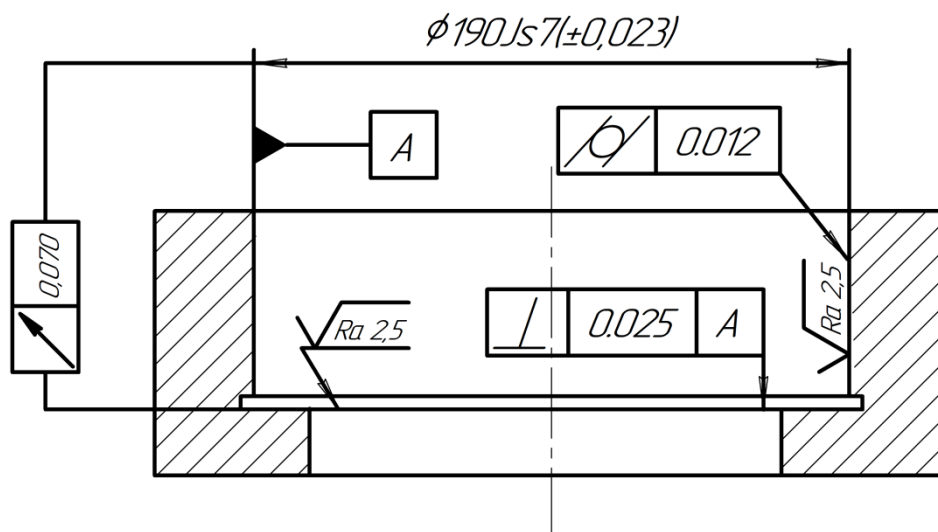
Обозначение допусков размера отверстия в корпусе
